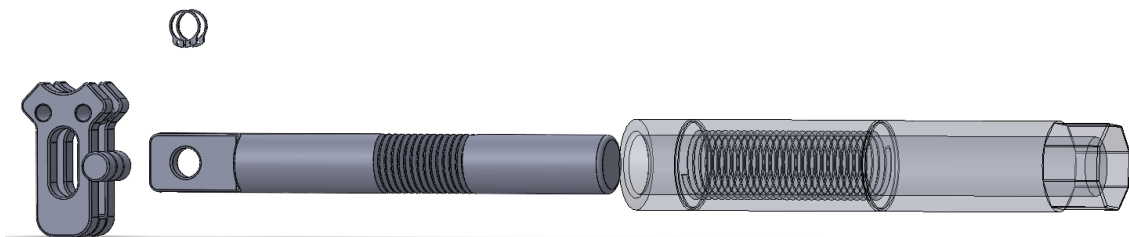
Vista explosionada del conjunto tornillo sin fin - actuador.
